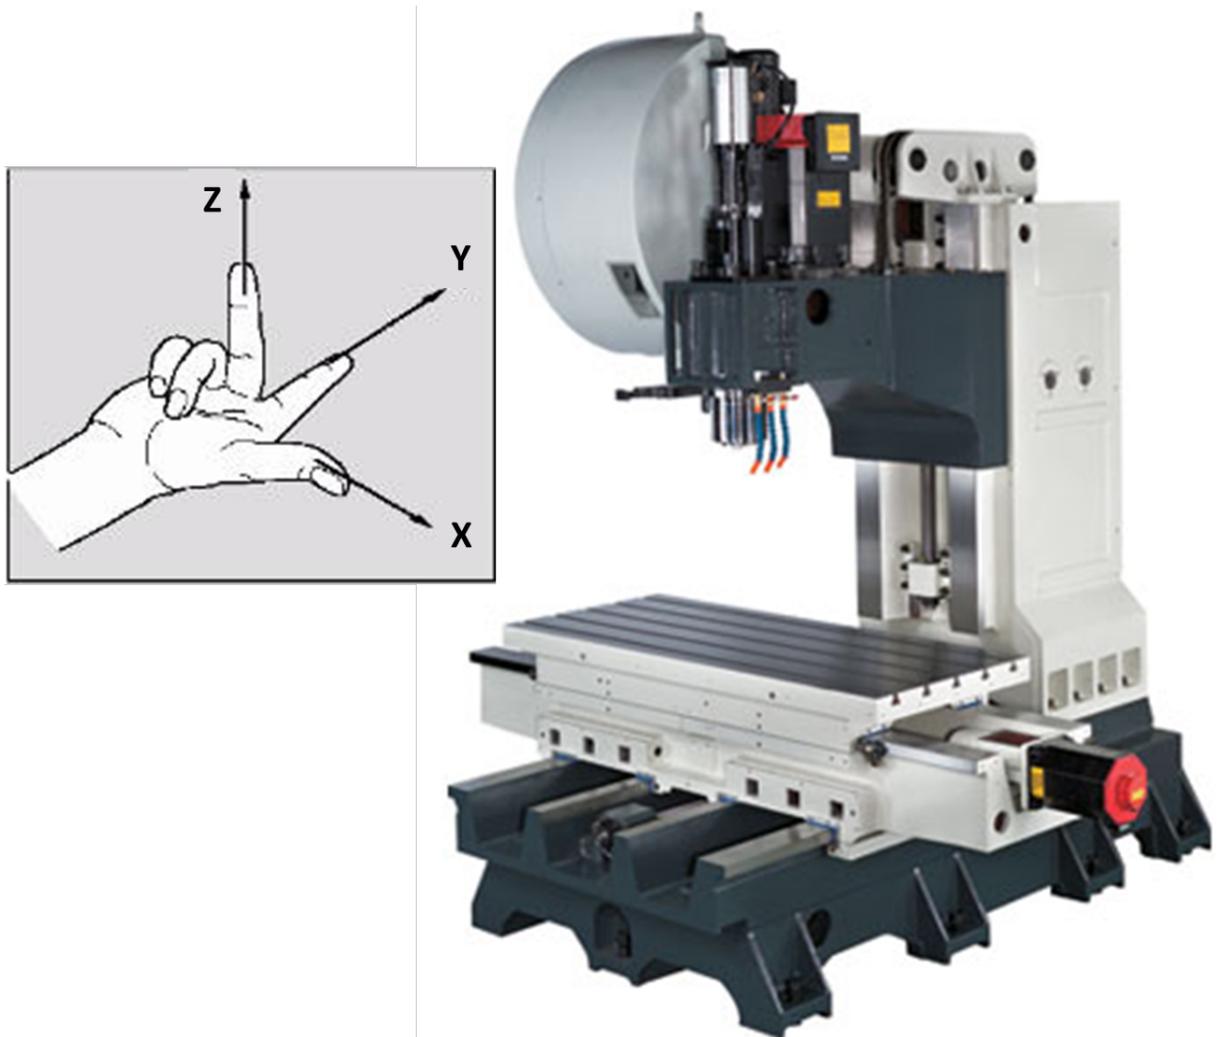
Sistema de coordenadas de um Centro de Usinagem CNC de 3 eixos
